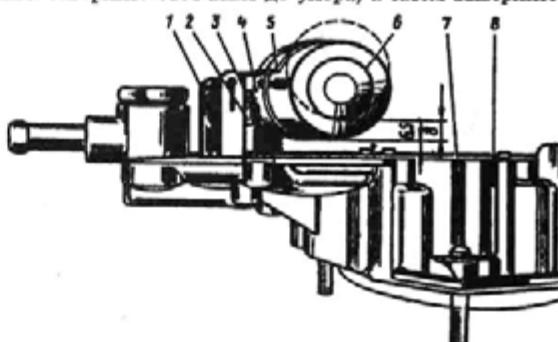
Установка уровня бензина в поплавковой камере карбюратора:
